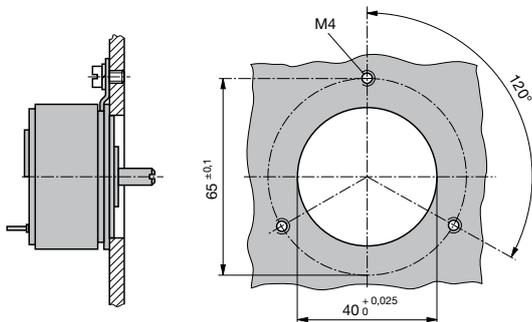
Bohrplan für Befestigung mit 3 Spannklemmern.
